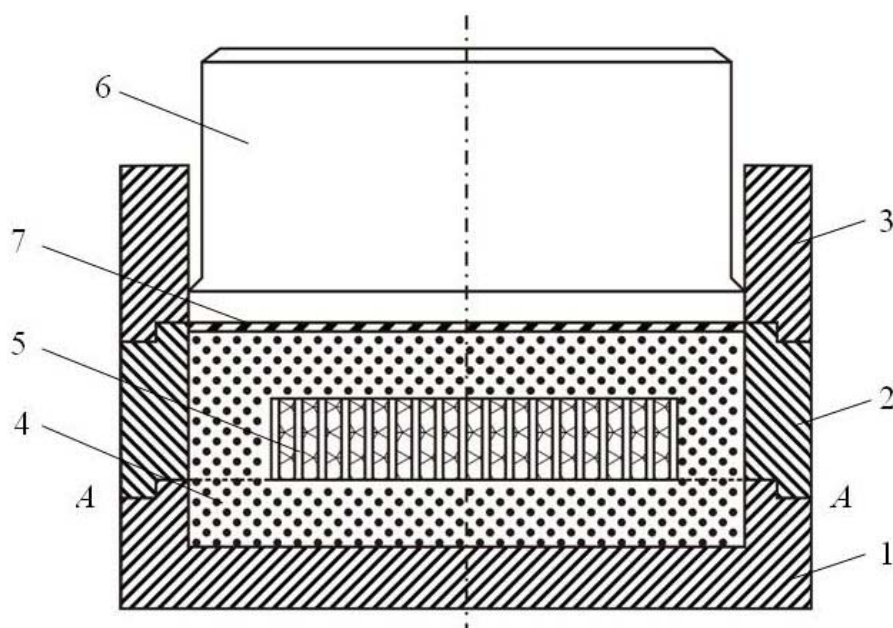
Схема реакционной цилиндрической пресс-формы диаметром 125 мм:
